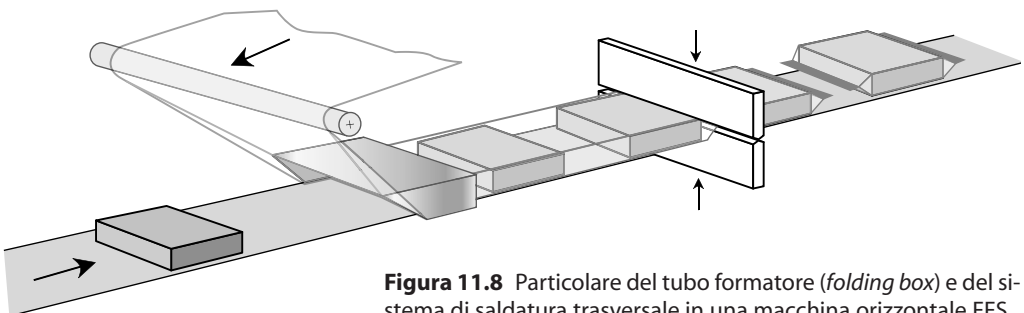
Particolare del tubo formatore (*folding box*) e del sistema di saldatura trasversale in una macchina orizzontale HFFS.
